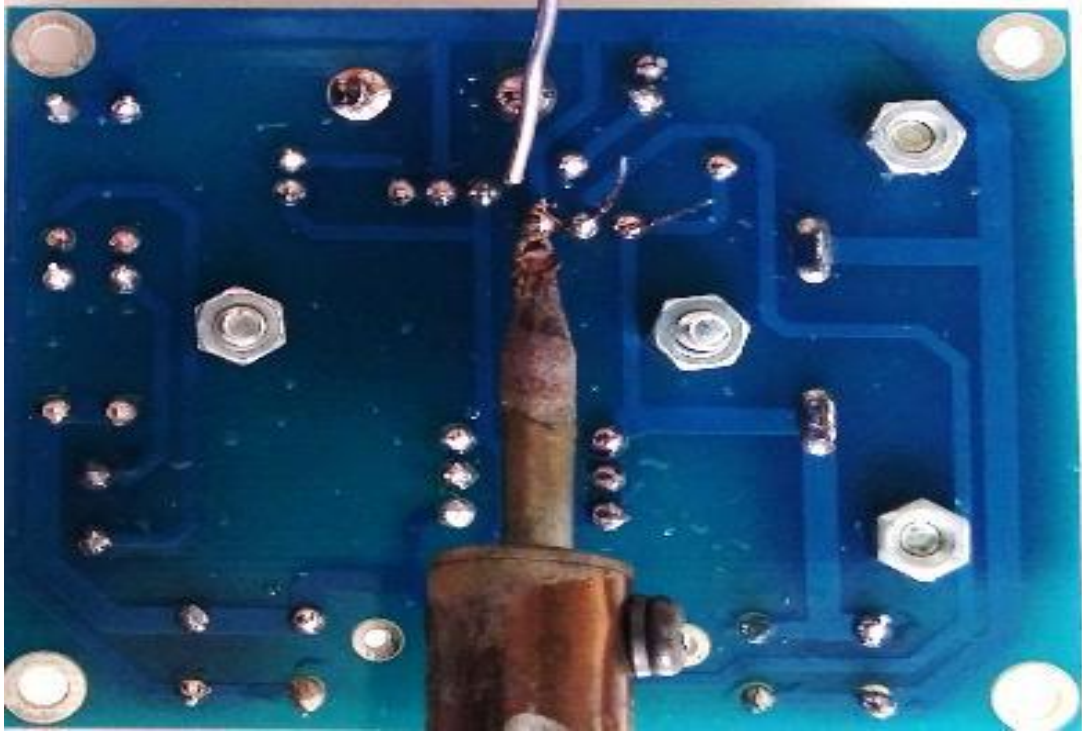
Güç kaynağı-2 klemenslerin montajı ve lehimlenmesi
